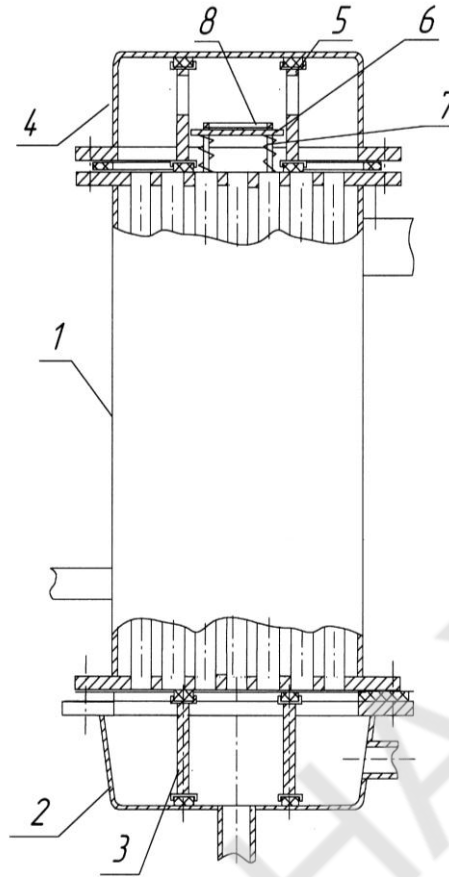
Кожухотрубчастий теплообмінник зі встановленими у ньому циліндричною і плоскою вставками: 1 – кожух; 2 – нижня колекторна камера; 3 – циліндрична вставка; 4 – верхня колекторна камера; 5 – отвори циліндричної вставки; 6 – перфорований диск; 7 – спрямовуючі стержні; 8 – кільцева основа.
